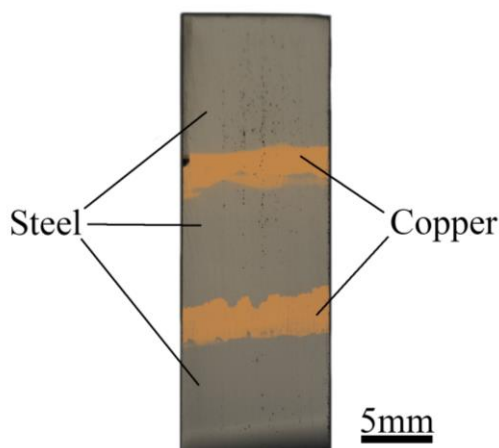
Двухкомпонентный полиметаллический образец сталь-медь
